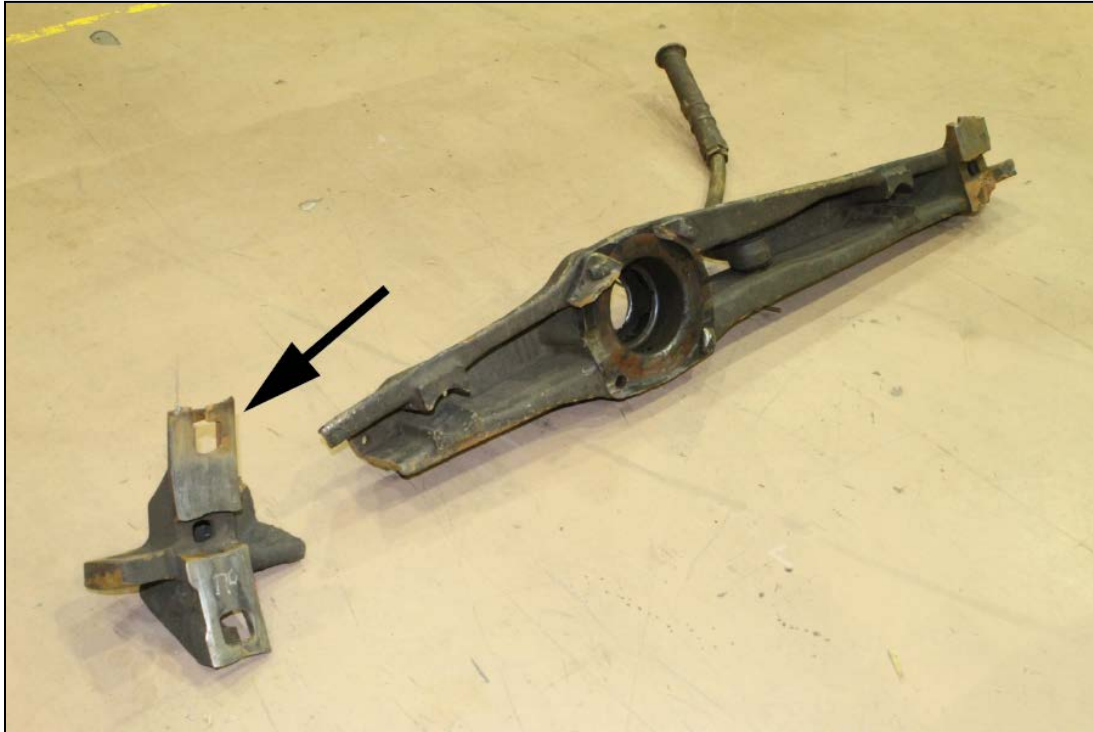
Poutre-frein sectionnée (Note : la tête de frein a épousé le profil de la bande de roulement.)
